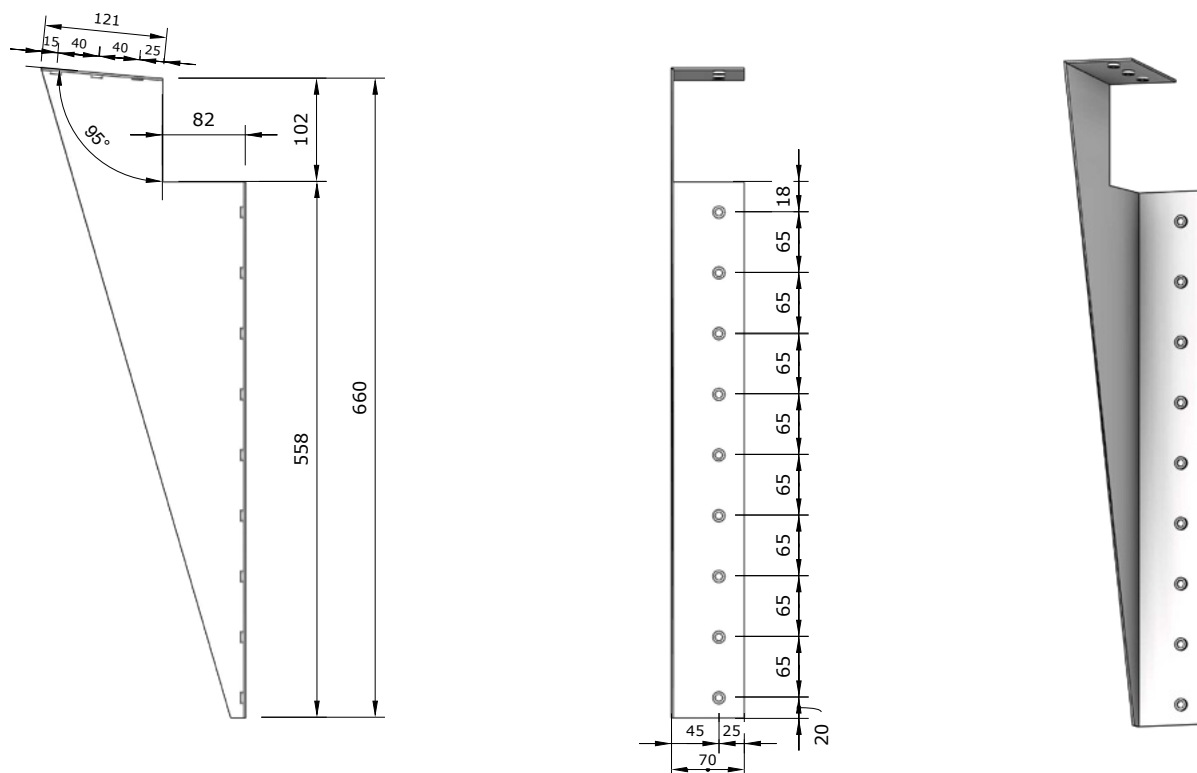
Vues de la tôle de support avec les dimensions de la fixation, dimensions en mm.
